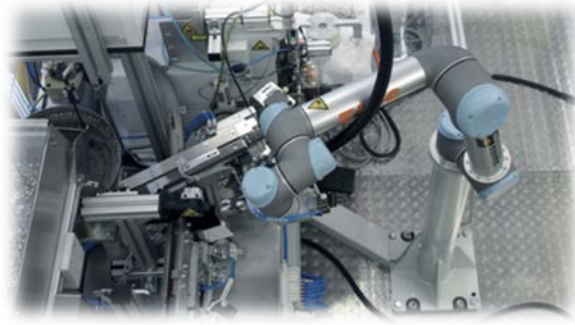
Brazo robótico capaz de realizar soldaduras blandas múltiples en piezas frágiles.
